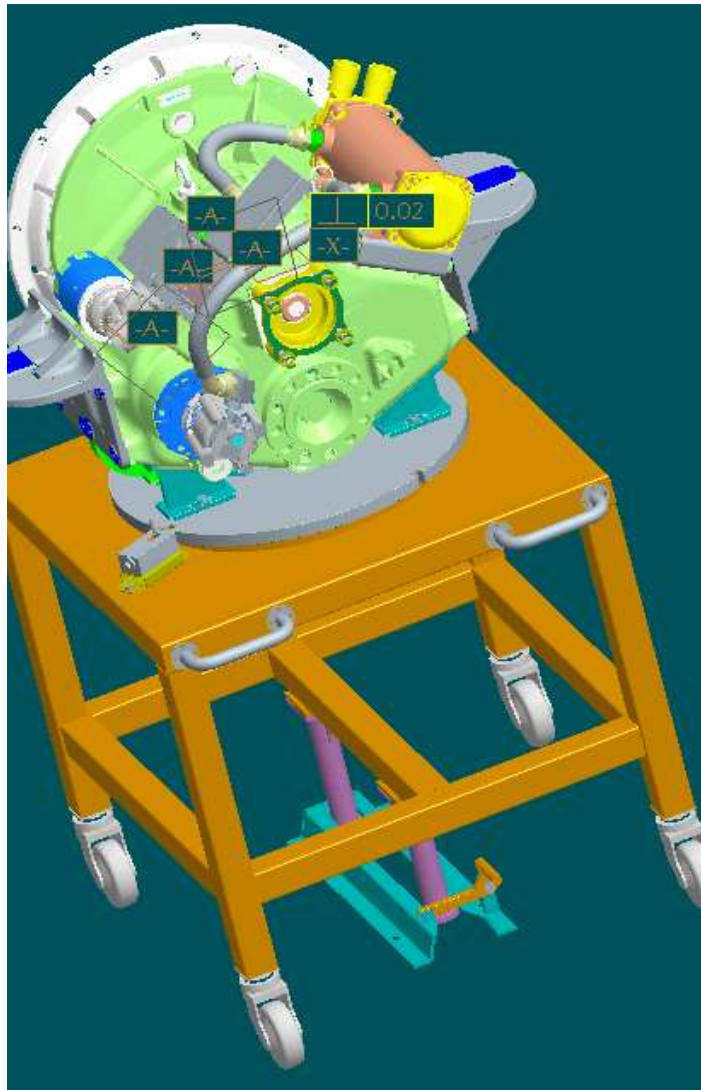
Carrello per il montaggio degli accessori.
